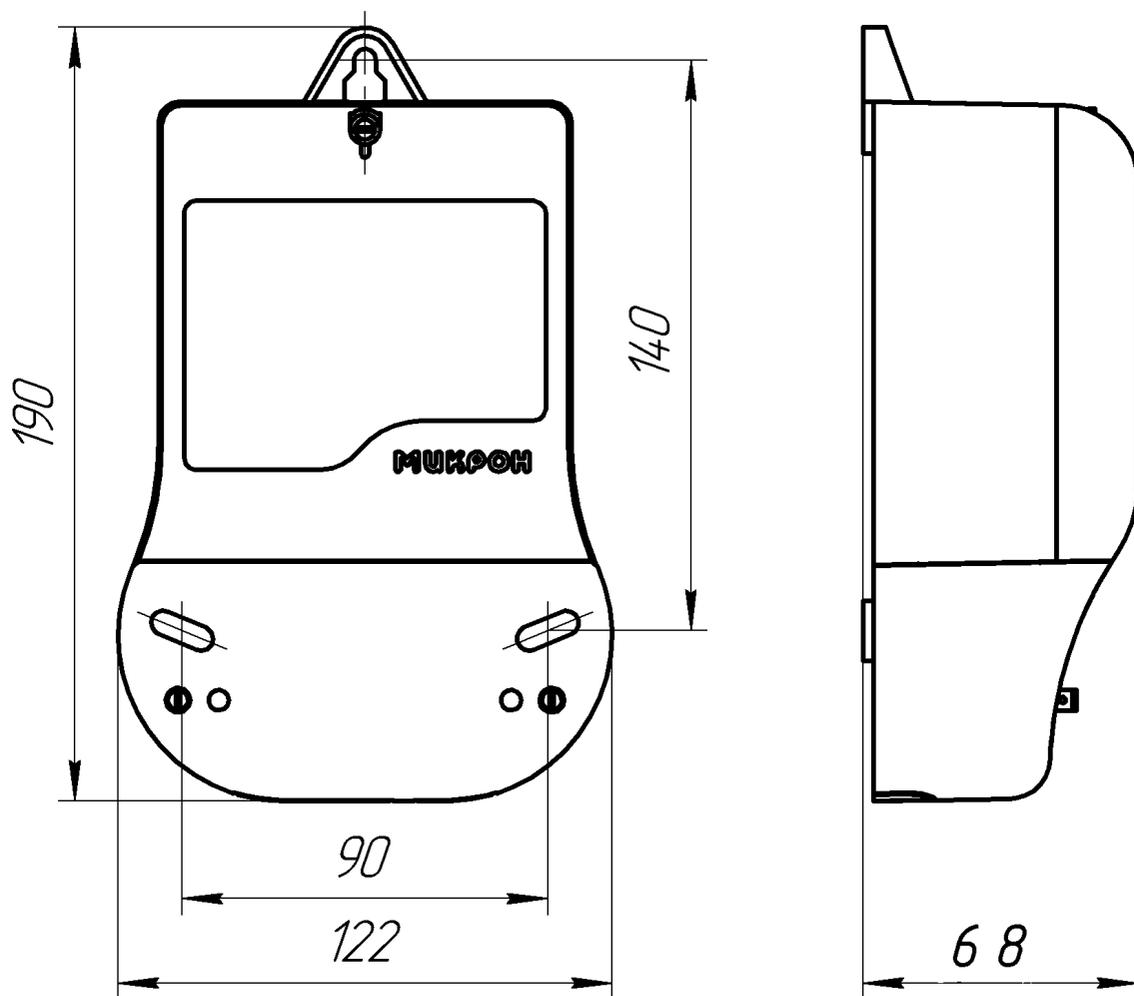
Габаритный чертеж и установочные размеры счетчиков
